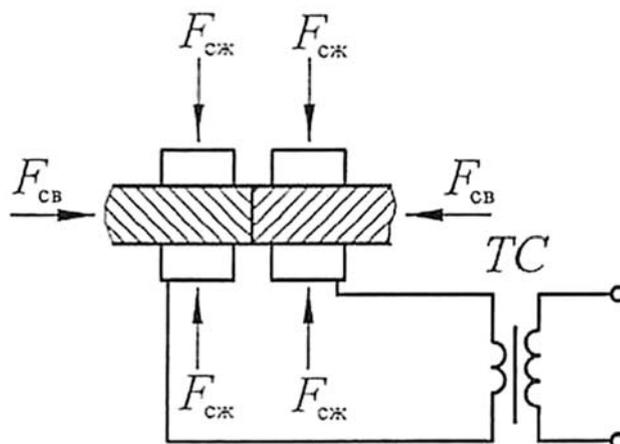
Упрощенная схема контактной стыковой сварки
